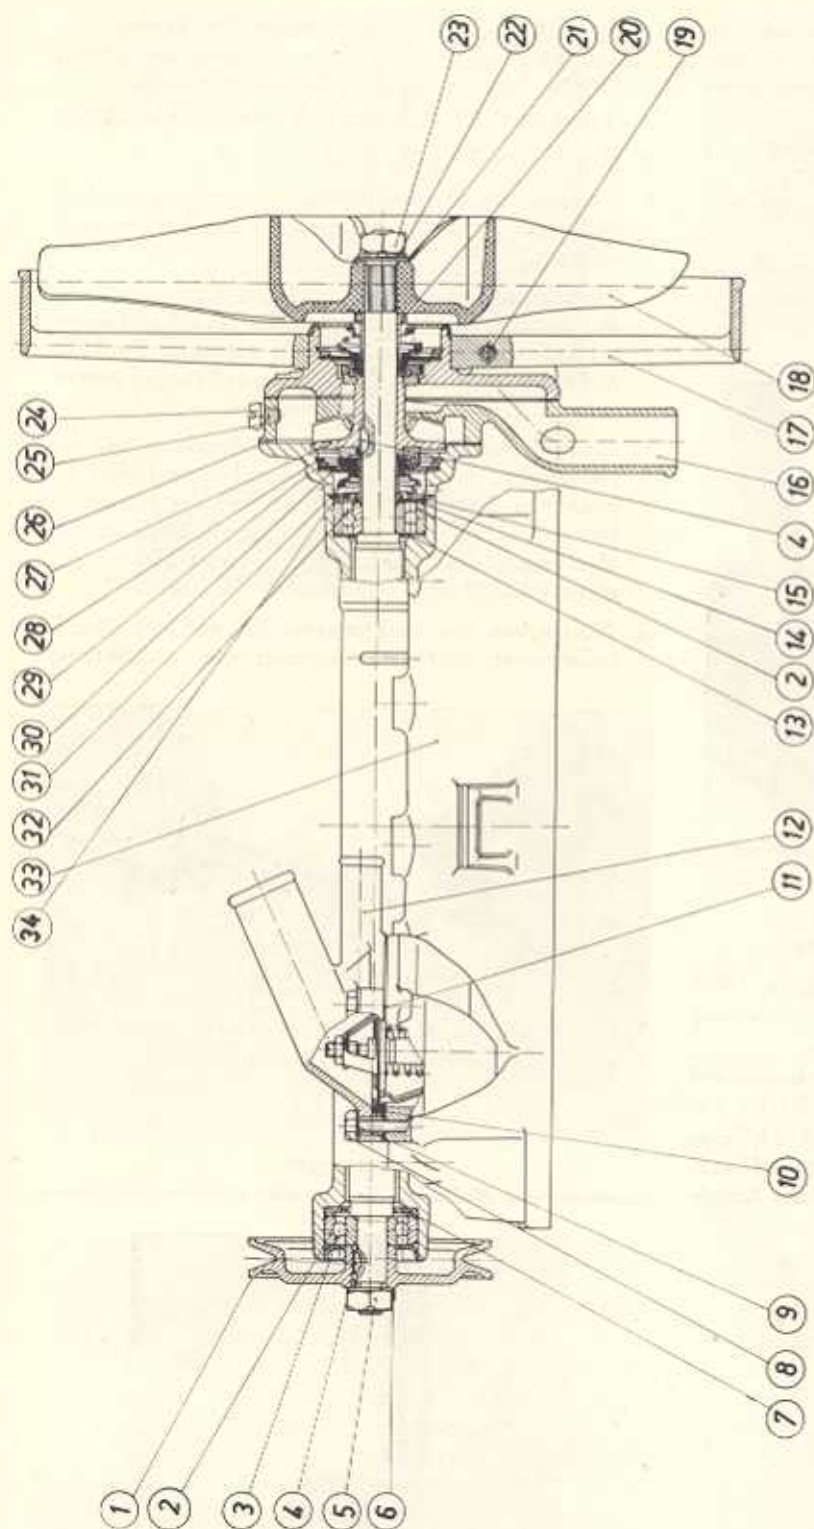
Zylinderkopf mit Einbauwasserpumpe (Schnittzeichnung)
